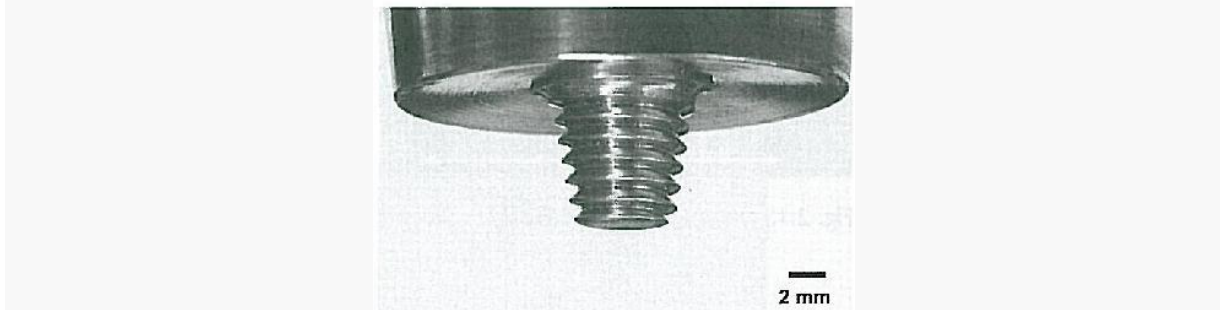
Типовий інструмент для зварювання з перемішуванням
